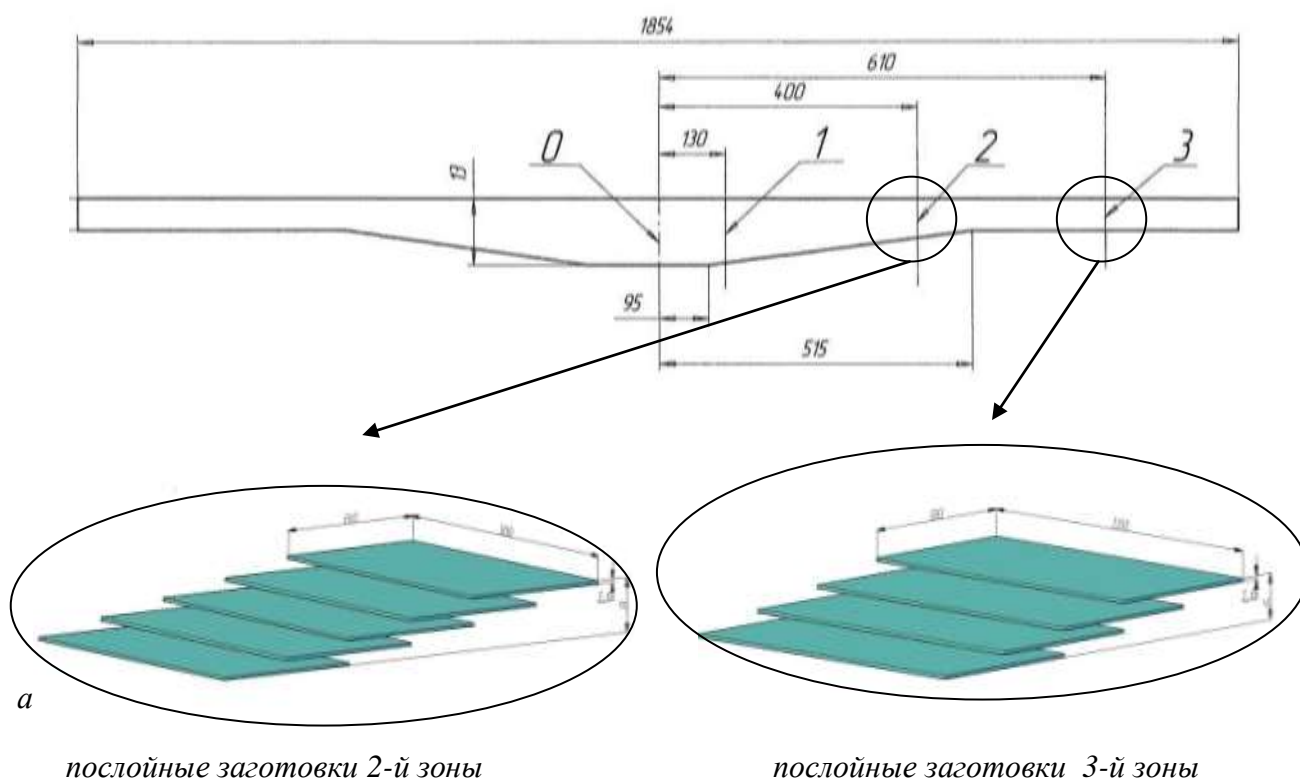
Расположение зон прокатанной полосы рессорного листа (а) для изготовления образцов из последовательных заготовок (б) со степенями обжатия ε :
